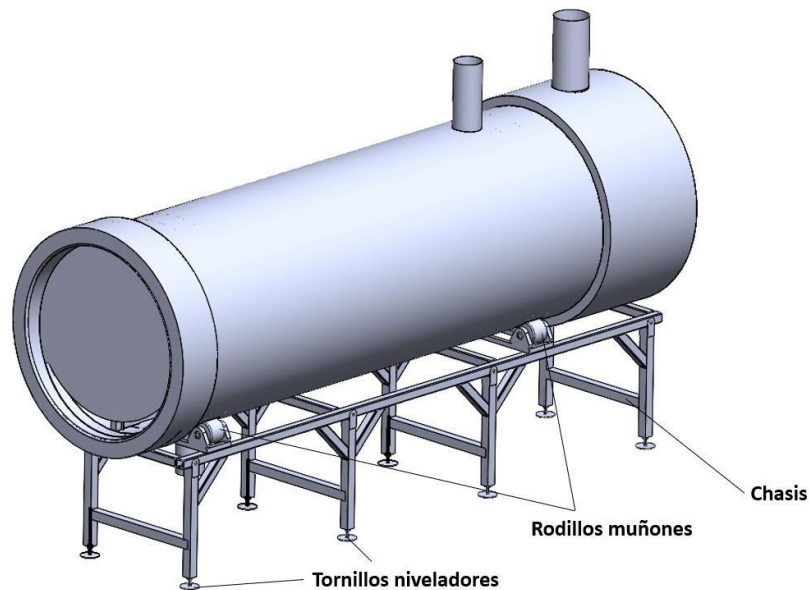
Ensamblaje final. Fuente: Elaboración propia (2023)
